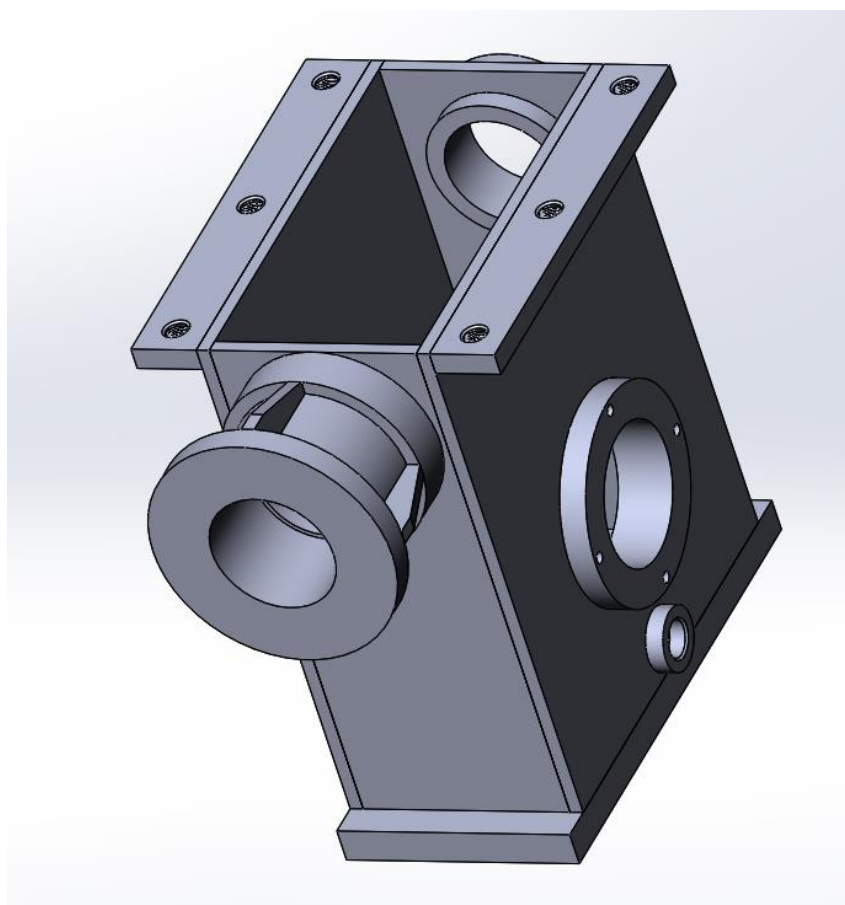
Трехмерная модель корпуса редуктора
